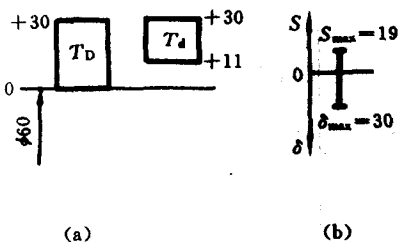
例 2.1 的尺寸公差带图和配合公差带图
